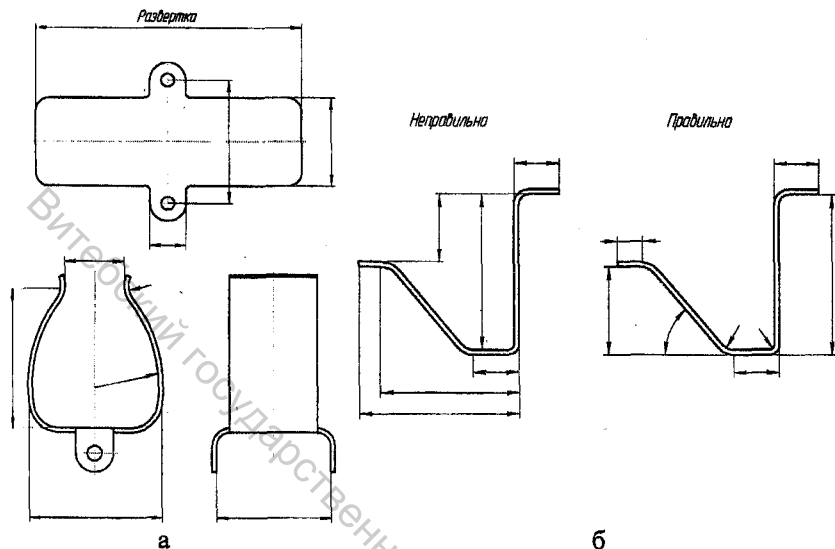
Схемы простановки размеров заготовок, полученных гибкой:
